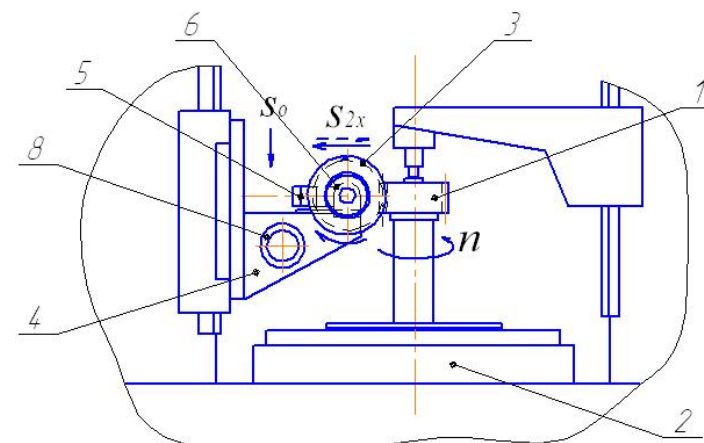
Робоча ділянка зуборізного верстата з керованими приводами для нарізання коліс за РК-способом:
